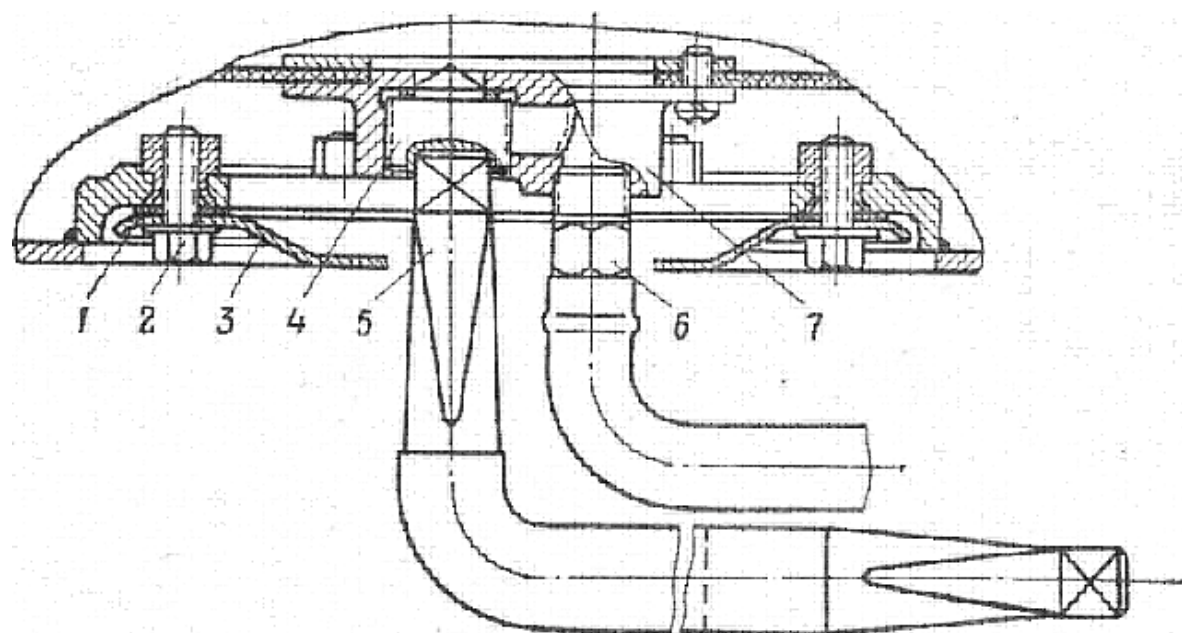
Установка ключа и шланга для слива топлива из топливных баков:
